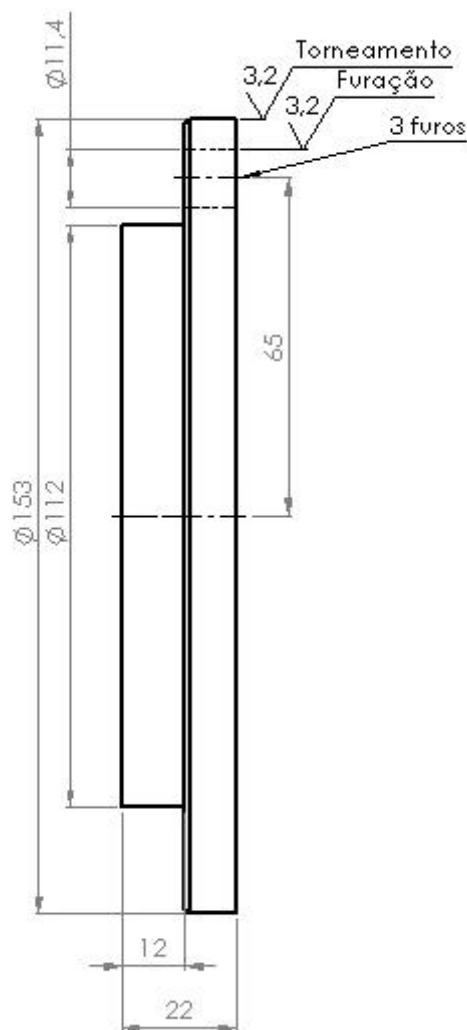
Flange do Acoplamento Após a Usinagem
